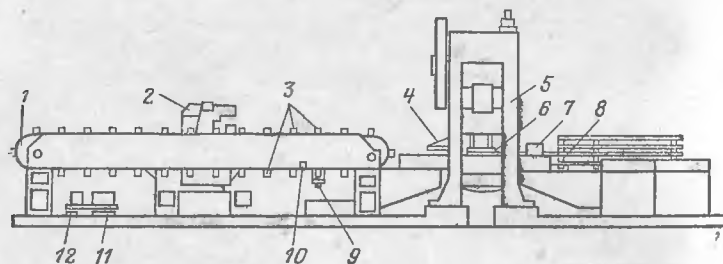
Автоматическая линия изготовления коллекторных пластин.
